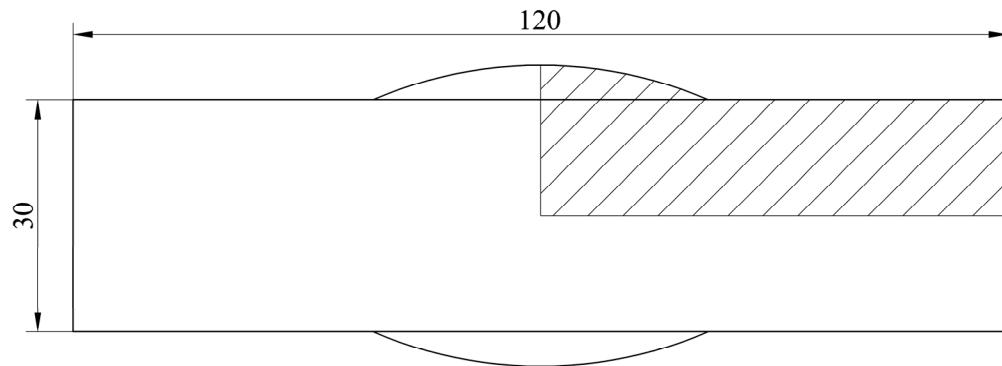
Схема симетричного з'єднання; розрахунковий переріз заштриховано
